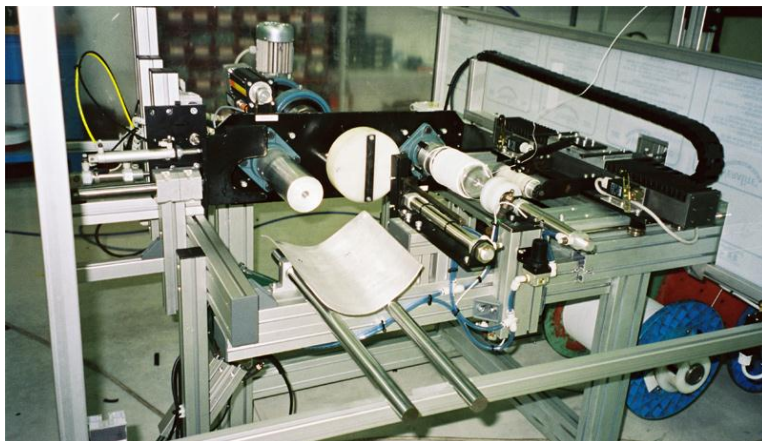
Camma elettronica di una bobinatrice (s.m.r.e. Engineering)
